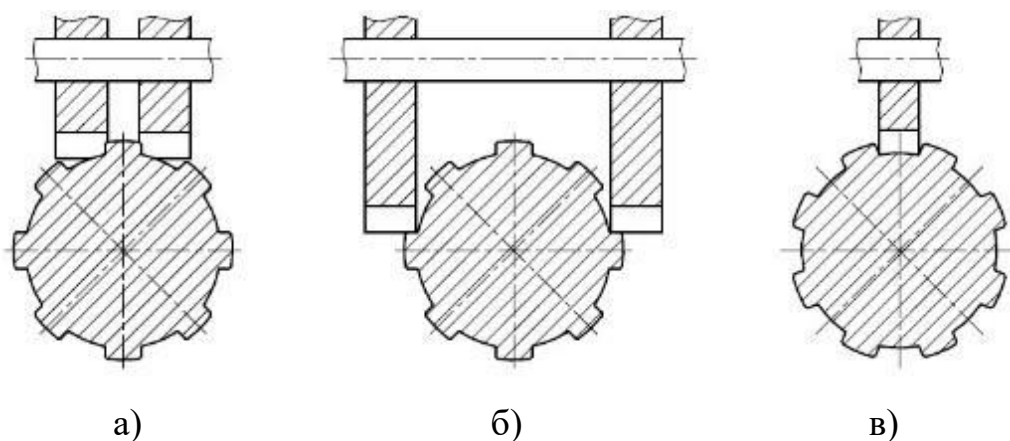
Схема фрезерування дисковими фрезами
